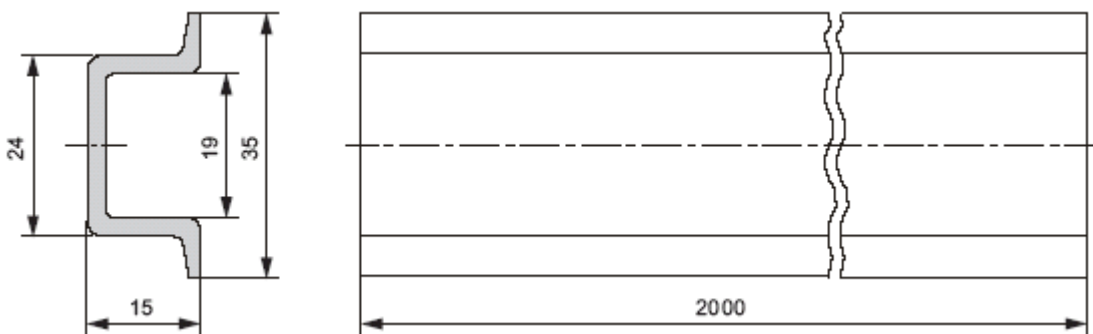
Габаритный чертеж 2000-миллиметровой стандартной профильной шины
